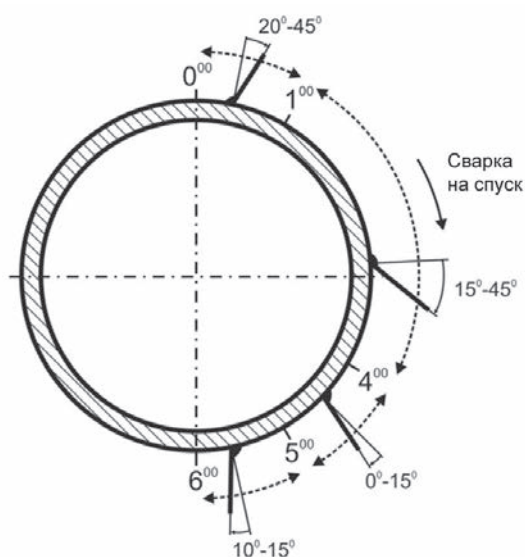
Схема расположения сварочной горелки при механизированной дуговой сварке в различных пространственных положениях корневого прохода
